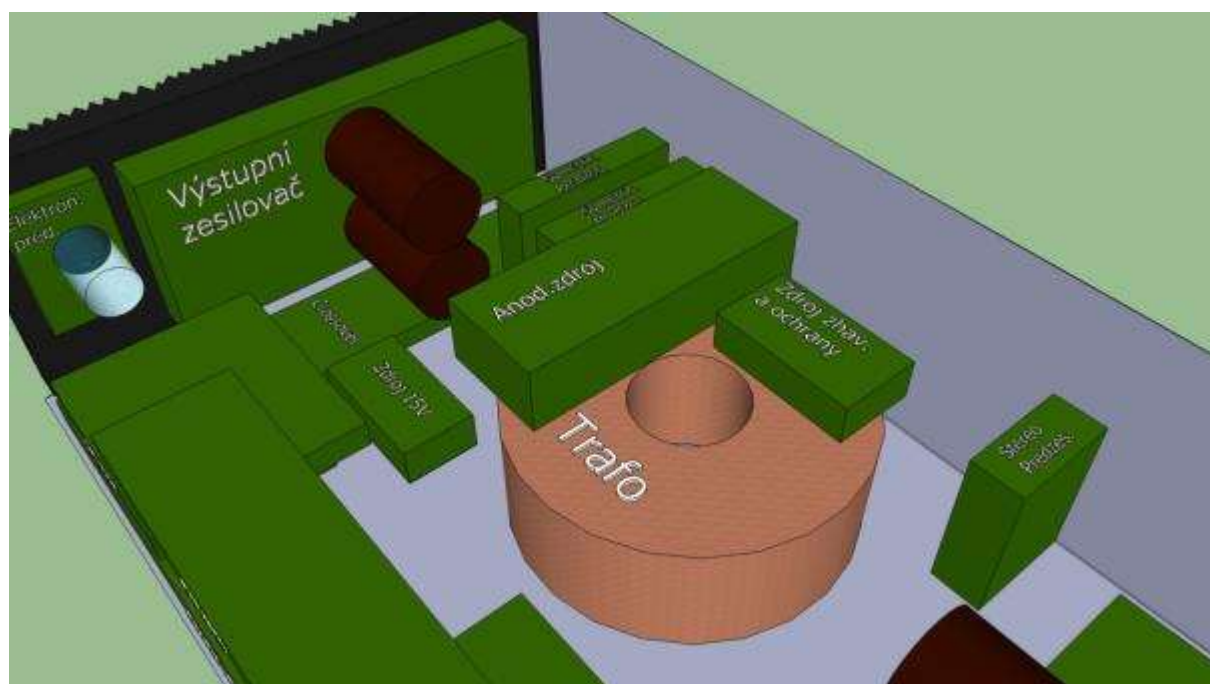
Rozmístění desek plošných spojů ve skříni: přední pohled
